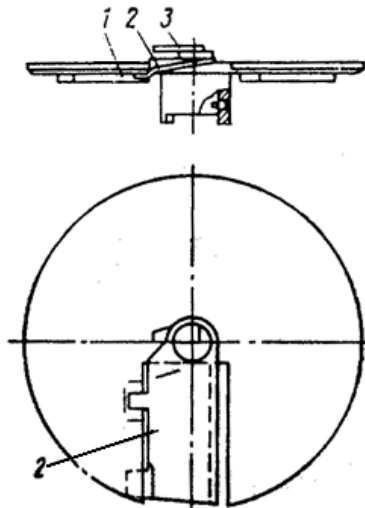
Верхній диск із ножем: 1-диск; 2-змінний ніж; 3-спеціальний болт для закріплення ножа
